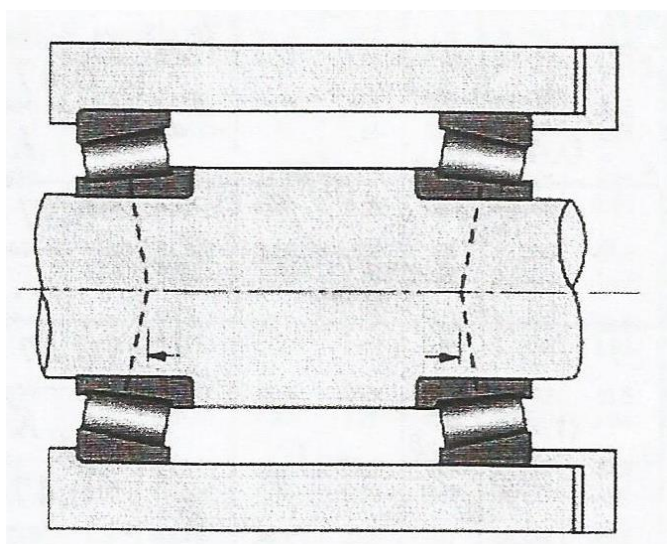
Montaje directo de rodamientos de rodillos cónicos
